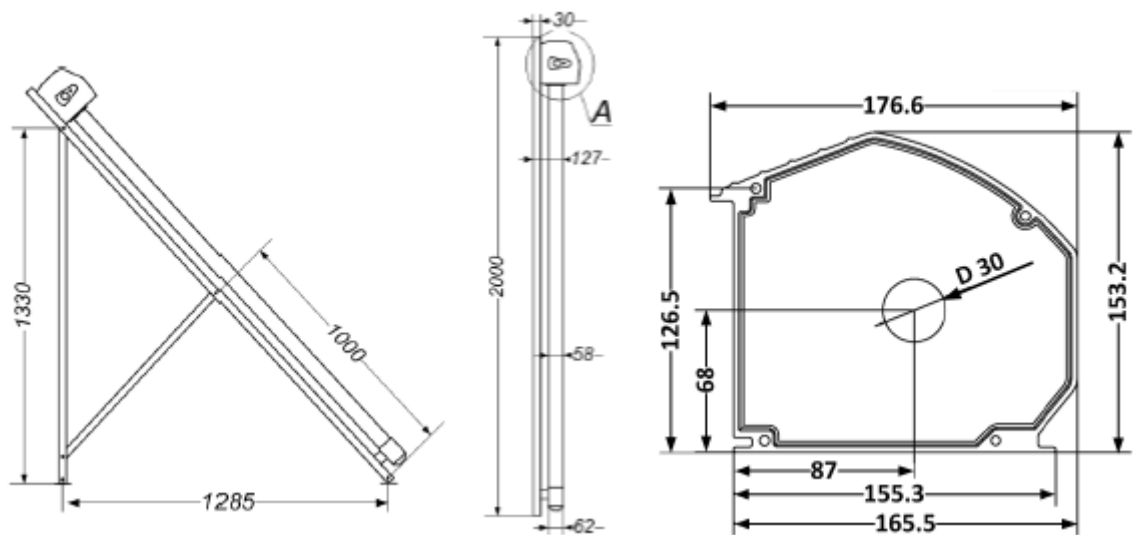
Основні габаритні розміри сонячного вакуумного колектора CBK-A
